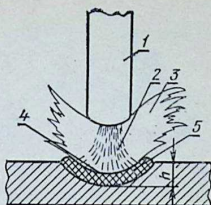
Схема установившейся сварочной дуги:
